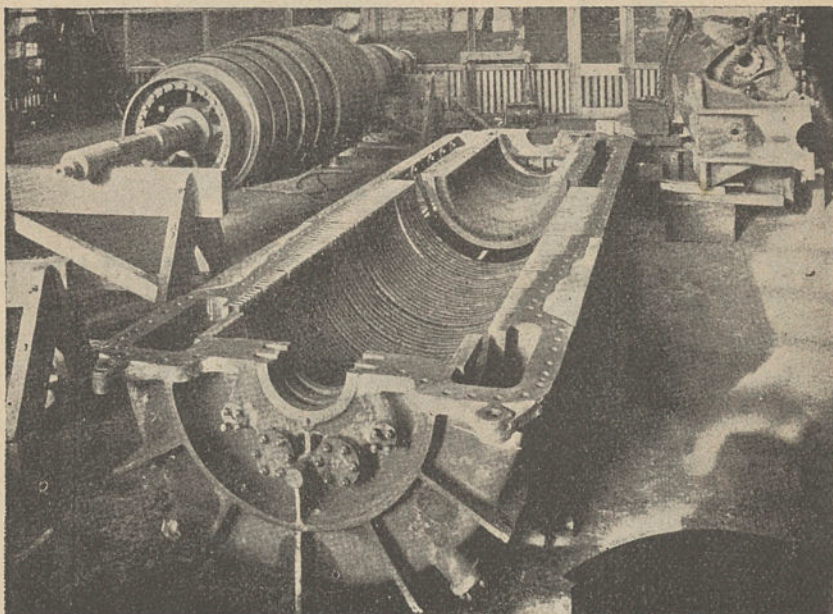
CYLINDRO E TAMBOR DE UMA TURBINA PARSON
